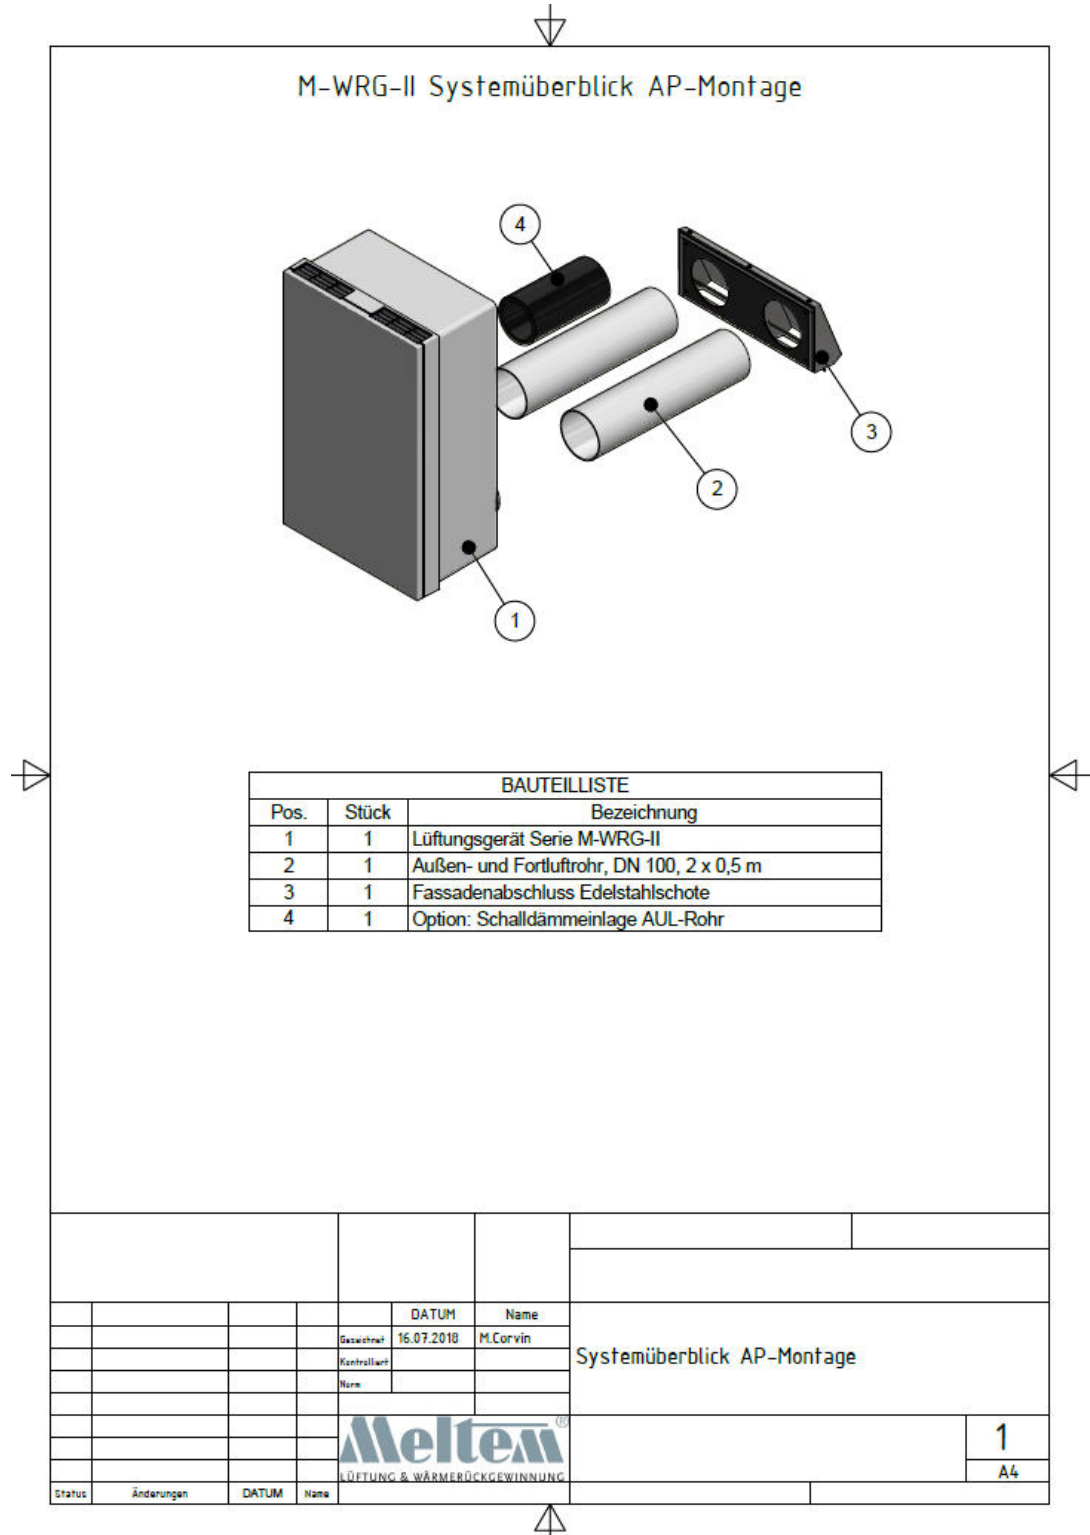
Explosionszeichnung des Lüftungsgerätes.
